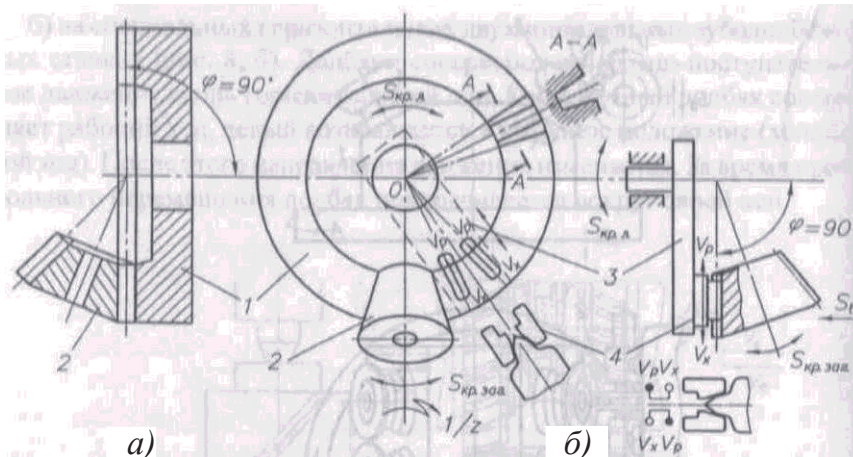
Схема формообразования при зубострогании: а – схема обката; б – схема движения рабочих органов зубострогального станка
